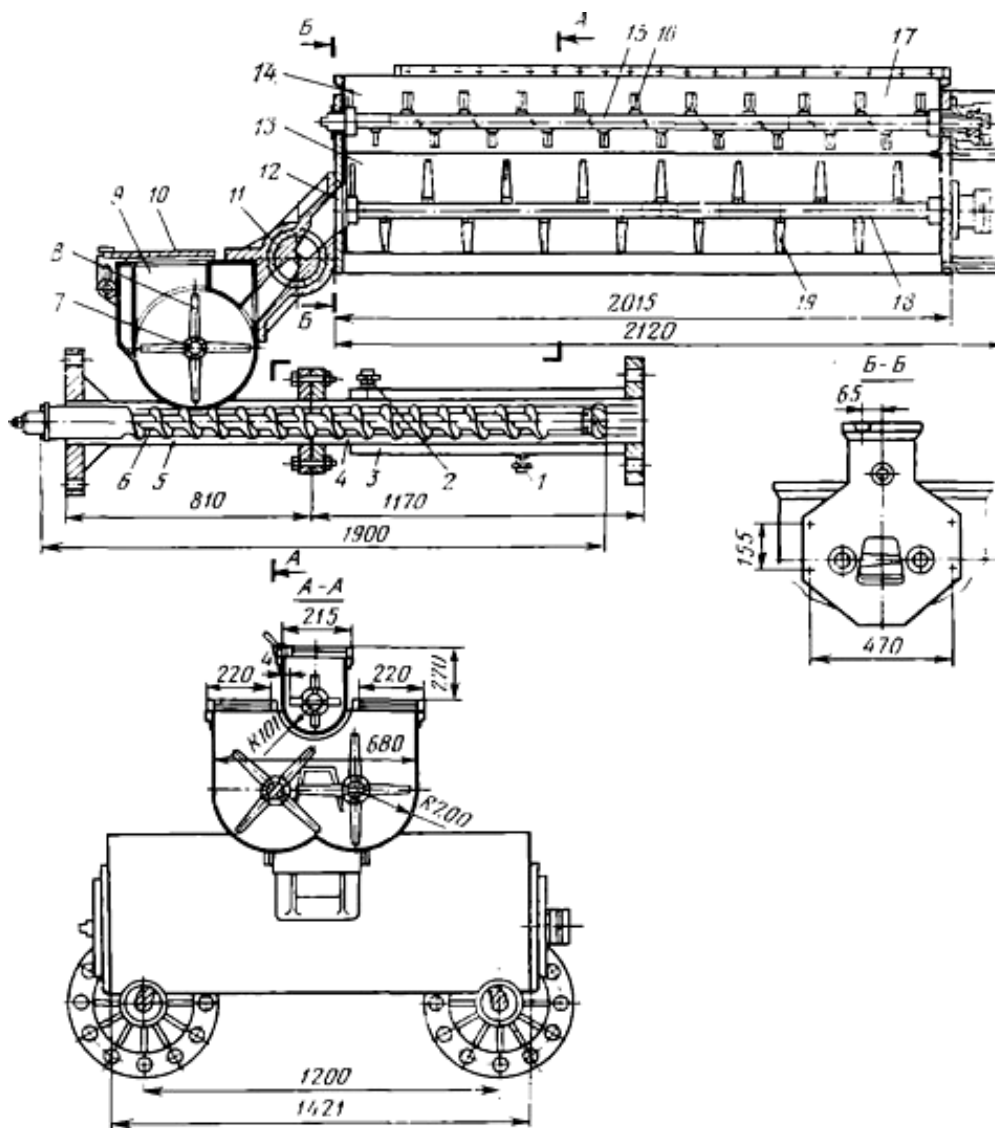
Тістозмішувач та пресувальний пристрій Б6-ЛПШ-750
